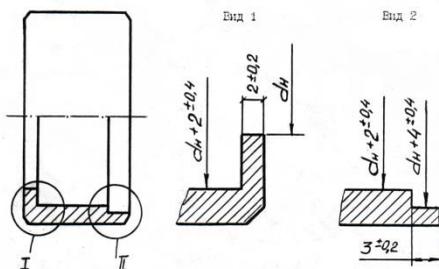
Основные параметры расточки внутренней поверхности втулок шарнирных сопряжений под запрессовку УУКМ
